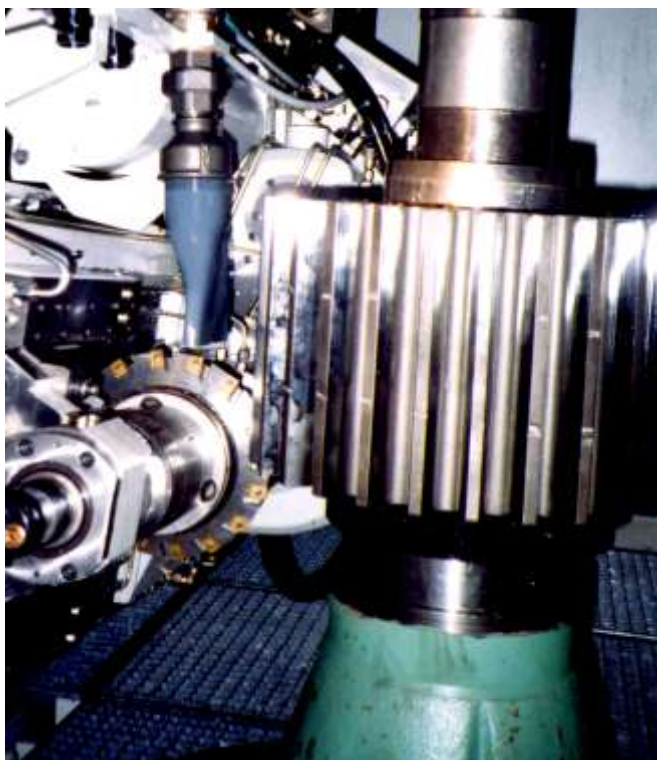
Обработка закаленного зубчатого колеса  $m=16 z=41$  на станке фирмы "Gleason-Pfauter"
